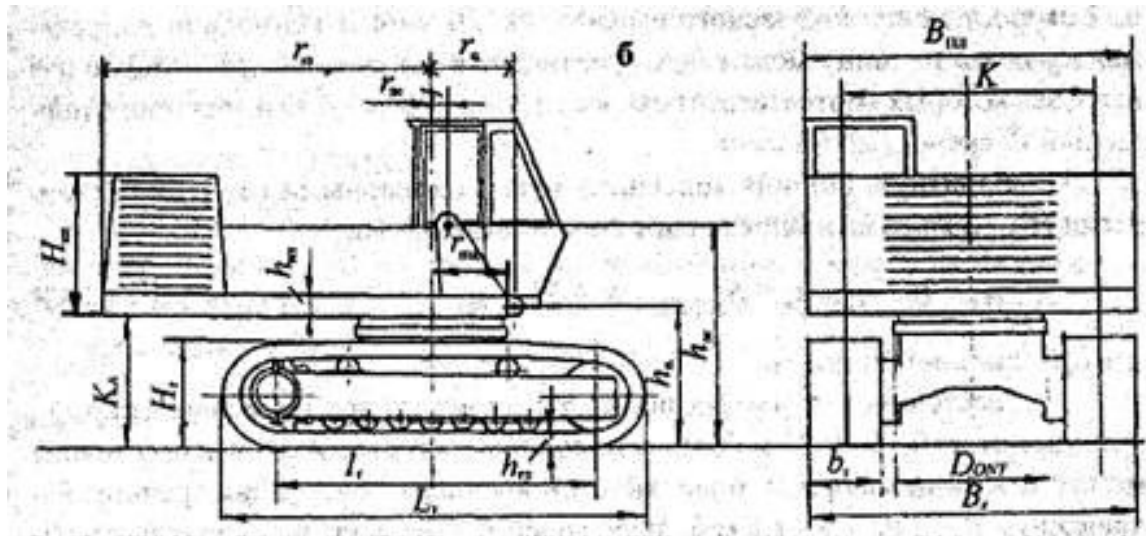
Схема розмірів базової частини одноковшевого екскаватора
